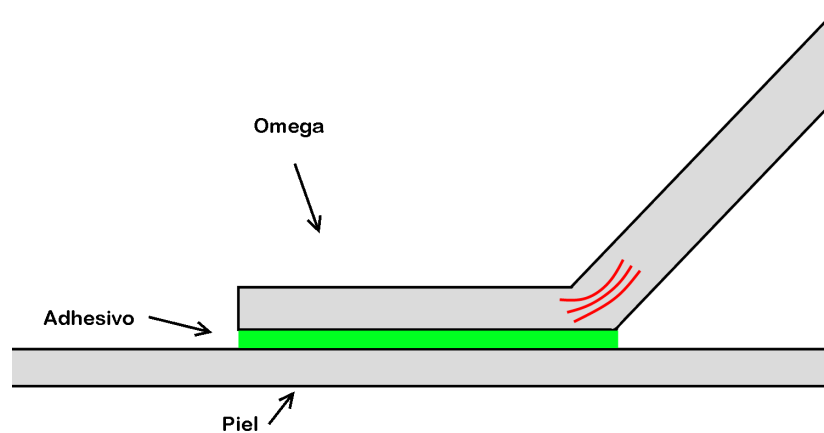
Detalle de la grieta inicial en C-C1
